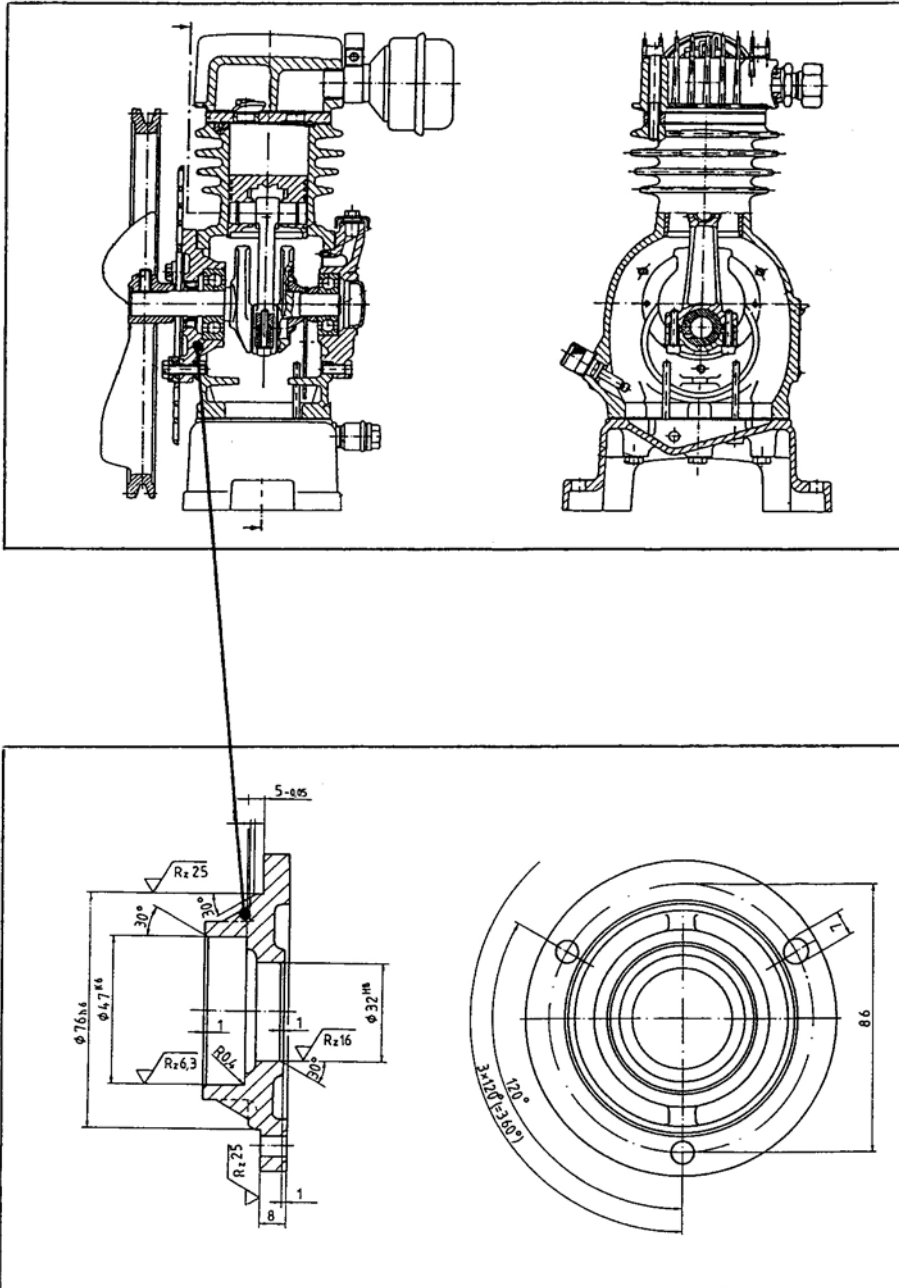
Gesamtzeichnung des Kolbenkompressors (oben) und Einzelteilzeichnung des Flanschlagers (unten)
